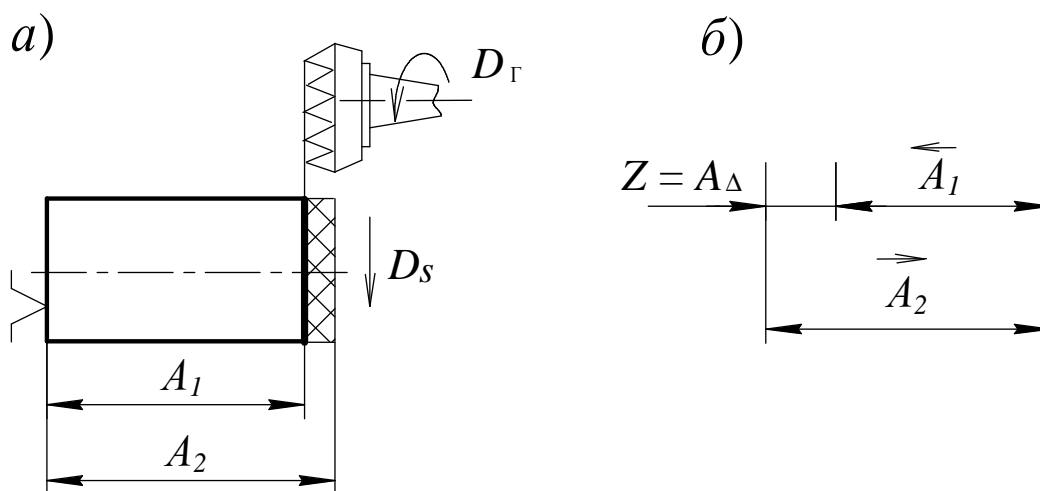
Схема фрезерования торца заготовки (а) и технологическая размерная цепь для определения припуска на обработку (б)
